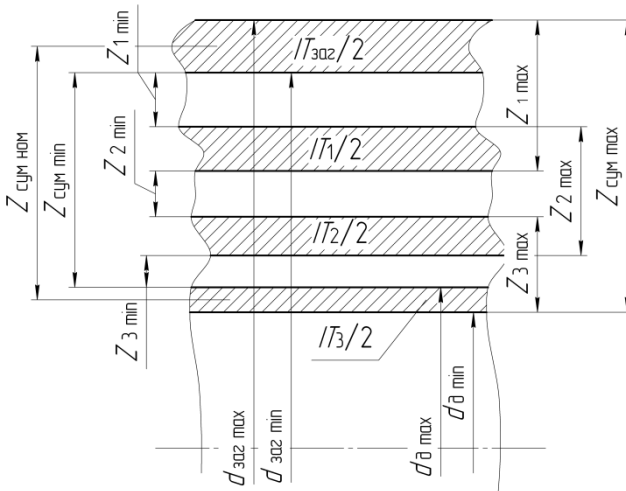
Схема розташування проміжних припусків і допусків на проміжні та початкові розміри заготовки для обробки зовнішньої поверхні обертання у разі послідовного наближення розміру до його потрібного значення
